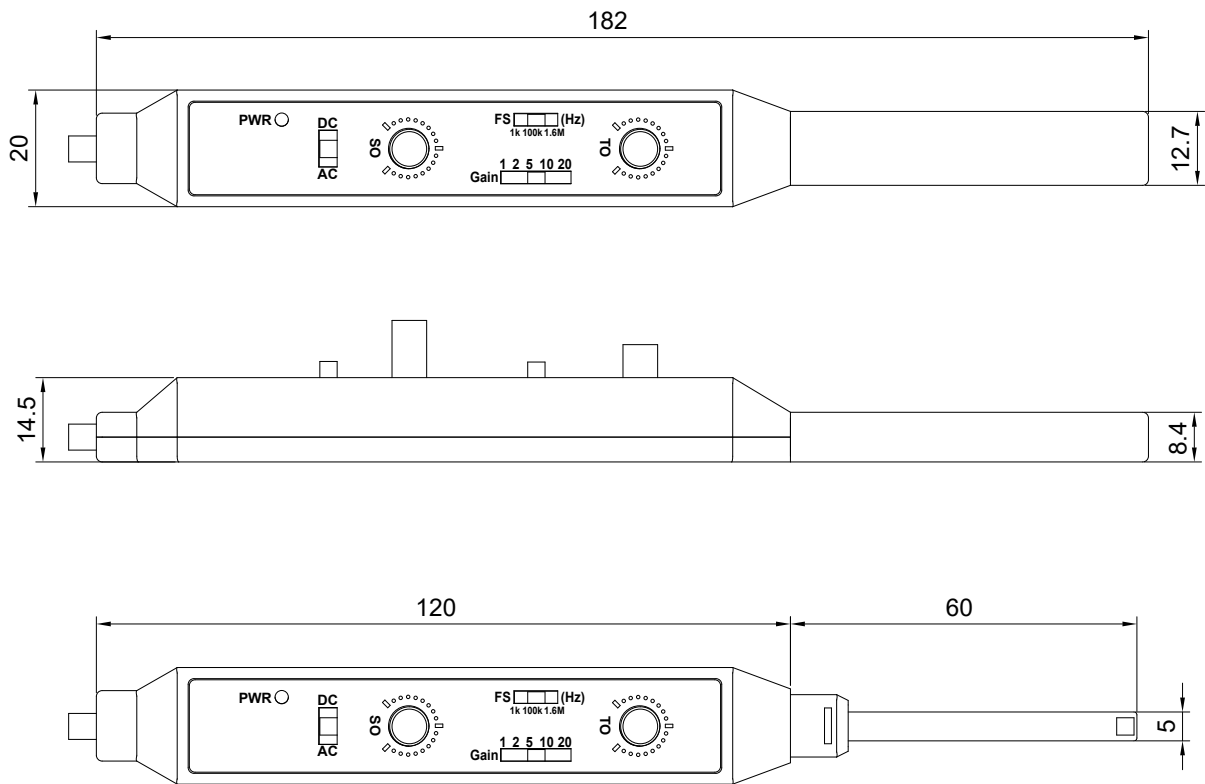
HFM2905 外形尺寸图 (尺寸单位: mm)
